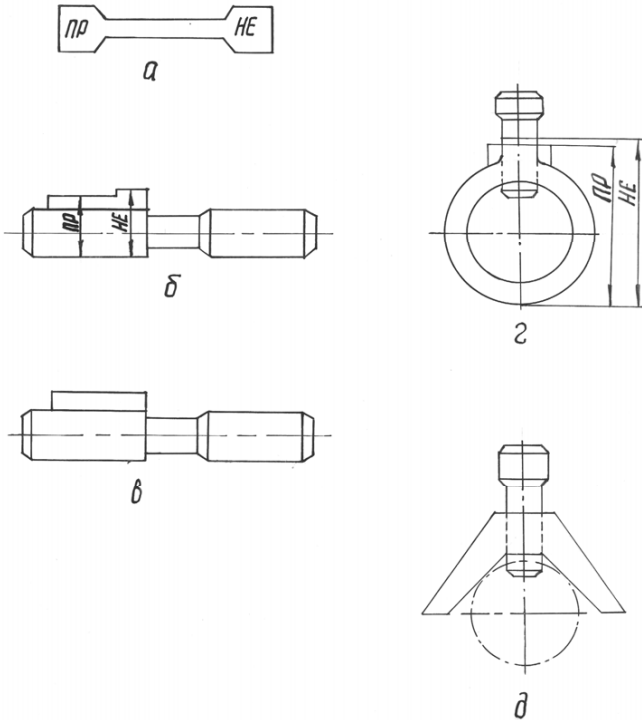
Засоби контролю шпонкових з'єднань: а – пластина; б – пробка із ступінчастою шпонкою; в – пробка із шпонкою; г – кільцевий калібр із стержнями; д – призма.
